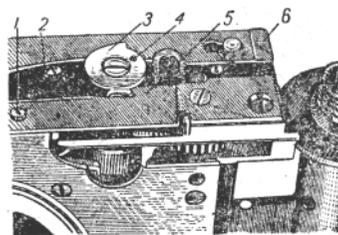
Нижняя сторона корпуса затвора. там расположен изогнутый конец пружины. Сама пружина не
